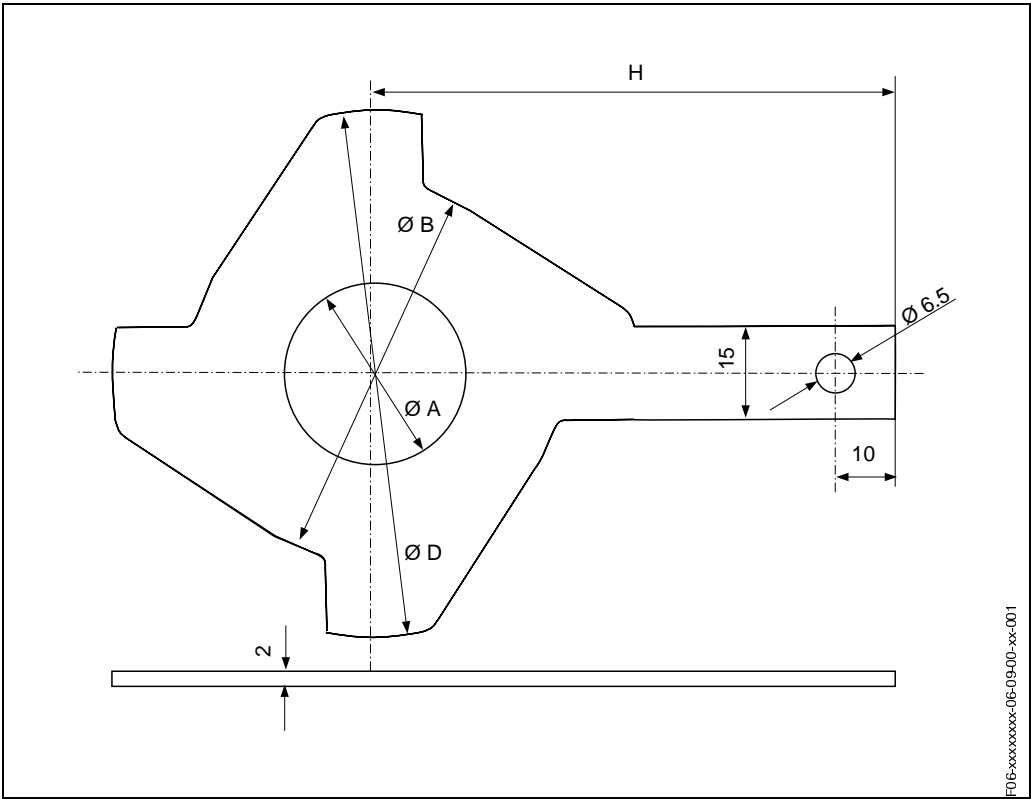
Dimensiones del disco de puesta a tierra DN 25...300 (promag W, P)
